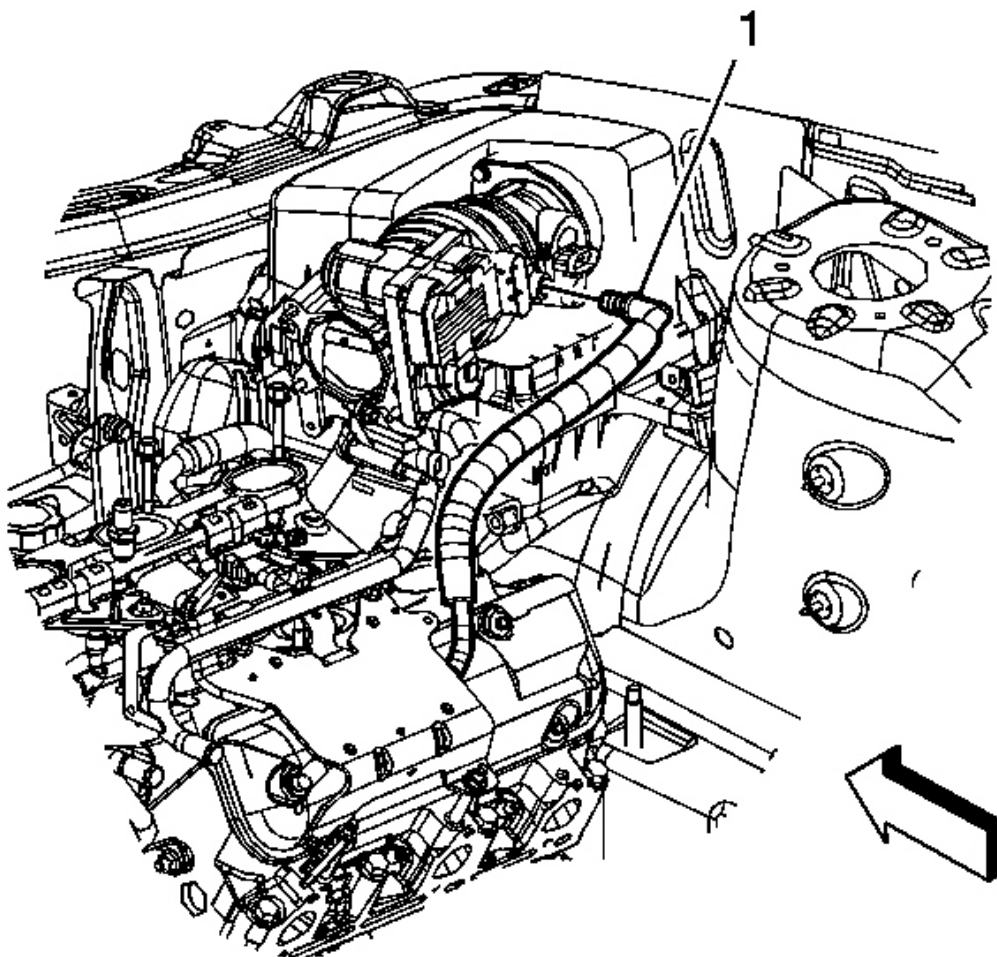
Vista de la válvula cubierta de balancines - Cortesía de General Motors Corp Izquierda.
